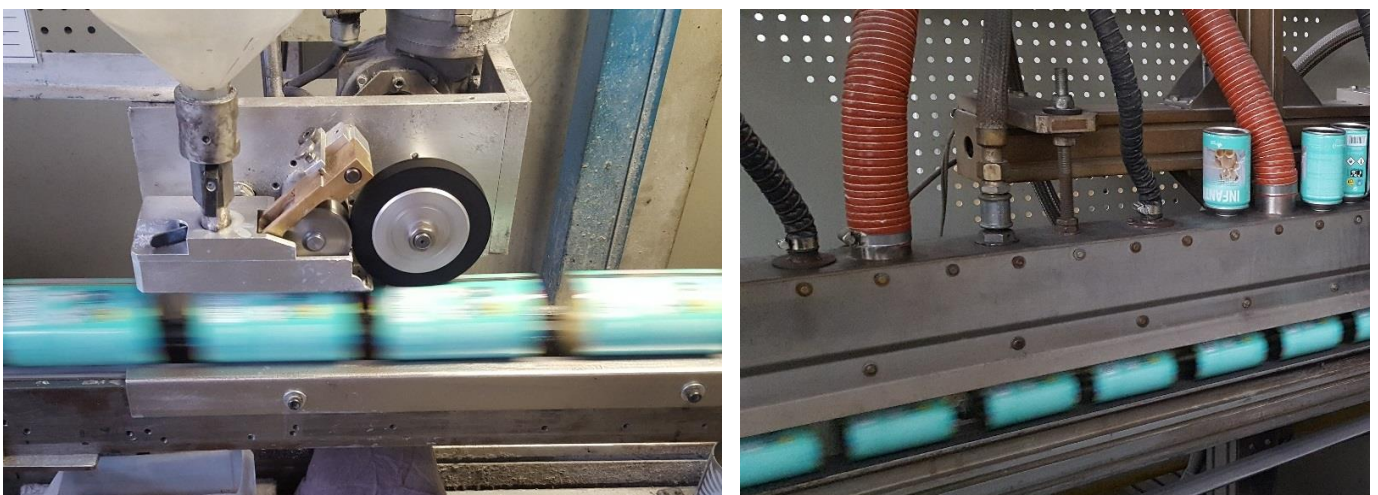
Adição e secagem do verniz no cordão de soldadura
